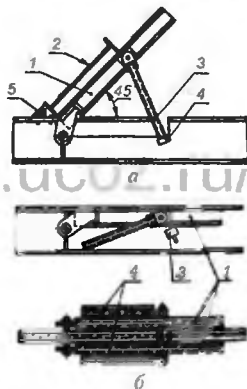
Пристрій для встановлення балок під зварювання:
